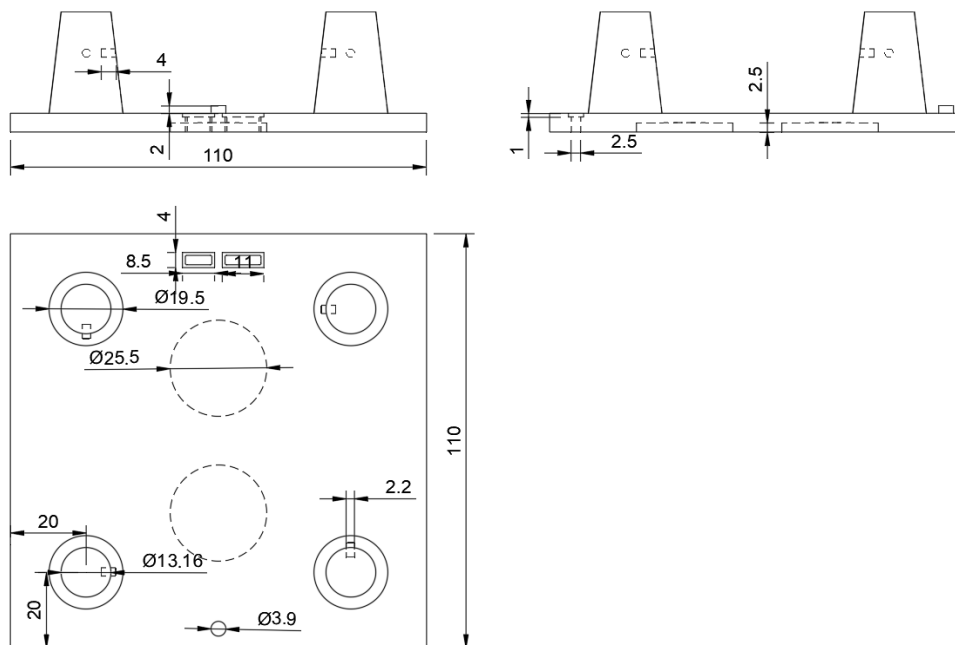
Ескіз основи інструмента маніпулятора
